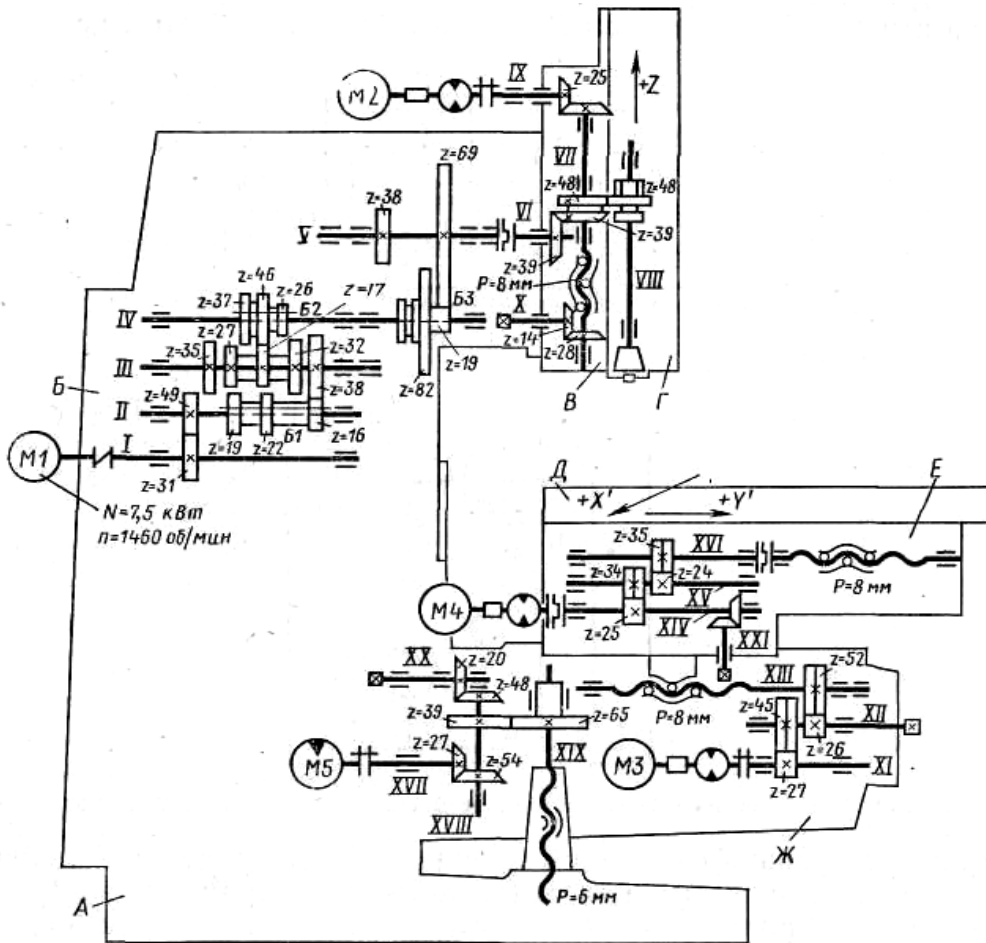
Кинематическая схема вертикально-фрезерного станка с ЧПУ модели 6Р13Ф3
